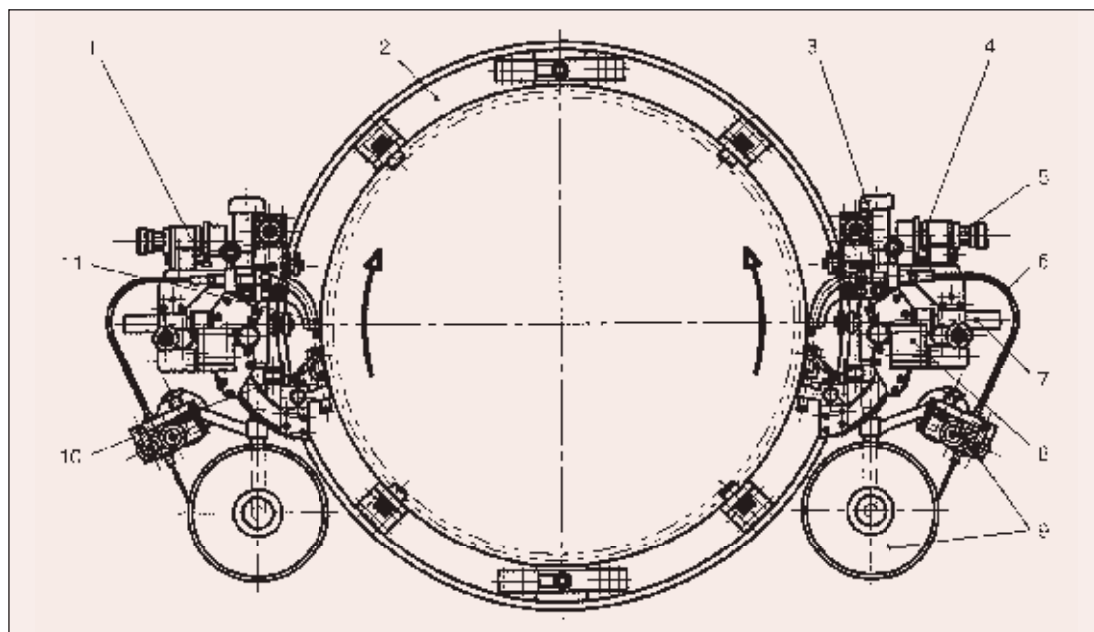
Автомат АД 365Т.01 для сварки неповоротных стыков труб порошковой проволокой с принудительным формированием шва: 1 — левая головка; 2 — разъемный рельс; 3 — тележка; 4 — правая головка; 5 — колебатель; 6 — направляющий канал; 7 — корректор; 8 — механизм разворота головки; 9 — блок подачи электрода; 10 — формирующий водоохлаждаемый ползун; 11 — мундштук
